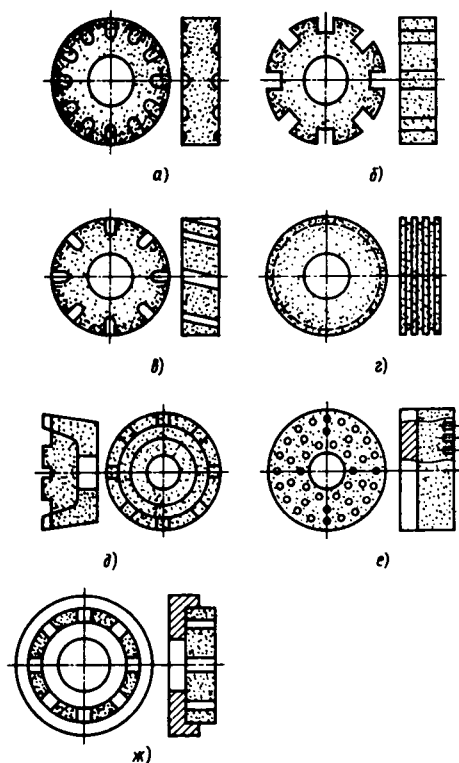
Круги с прерывистой рабочей поверхностью:
